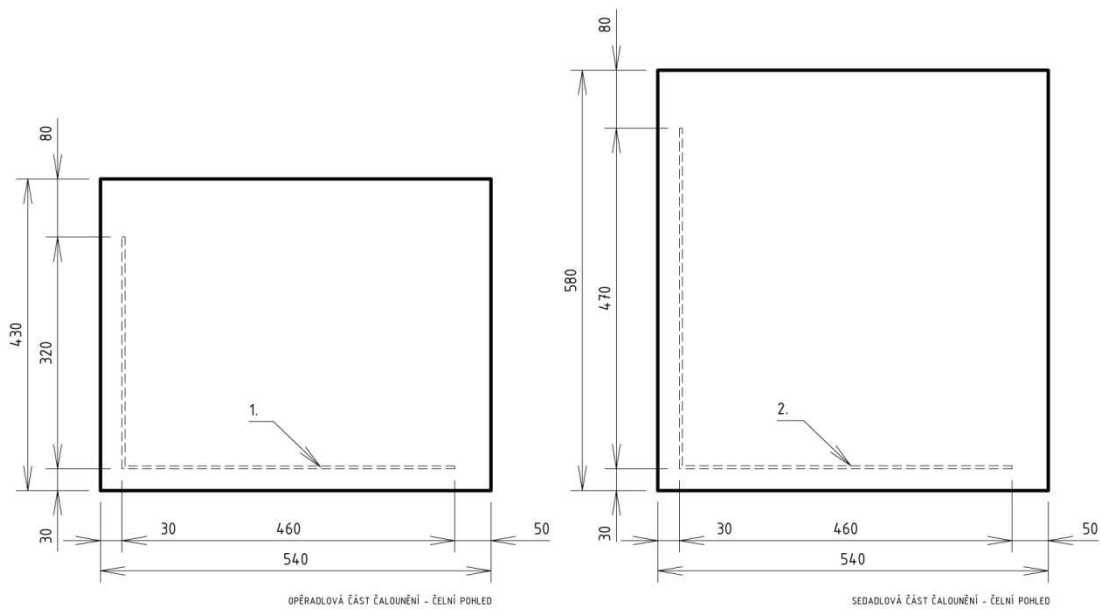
Schematické řezy konstrukcí čalounění – varianta 3
